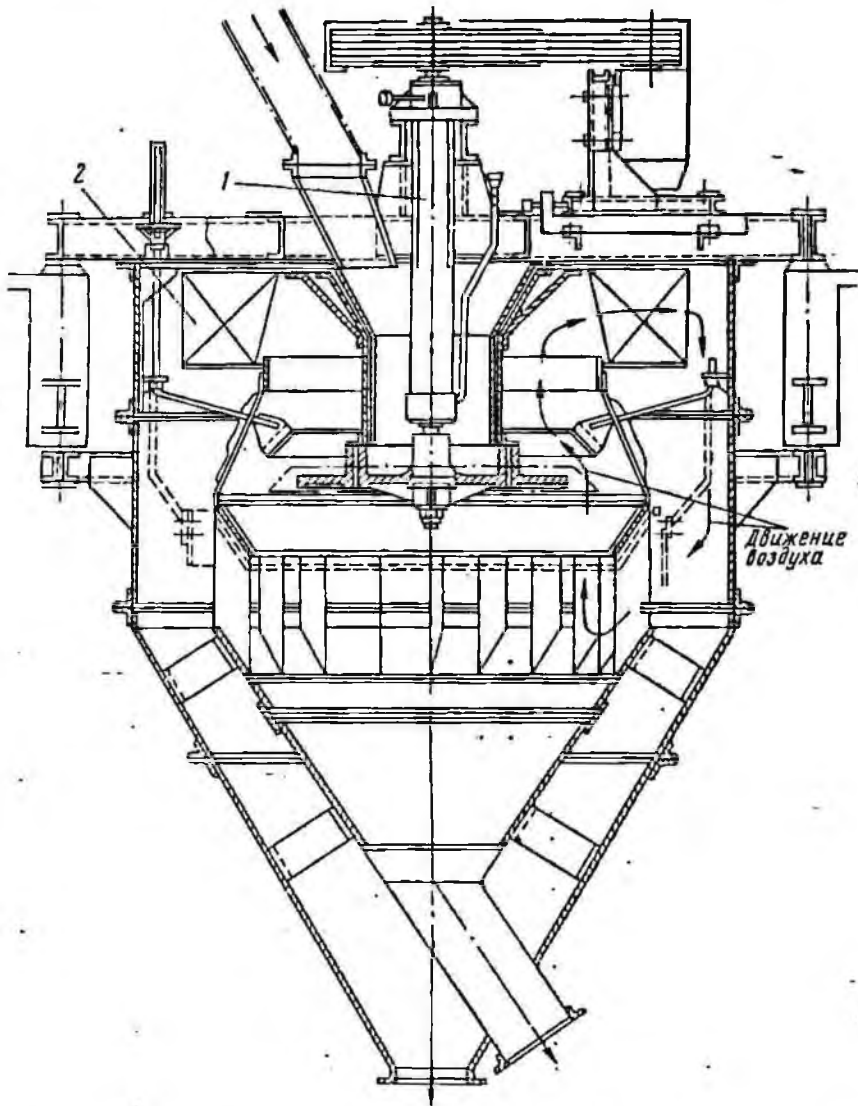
Внутрициркуляционный центробежный сепаратор для обеспыливания углей конструкции Гипрококса:
